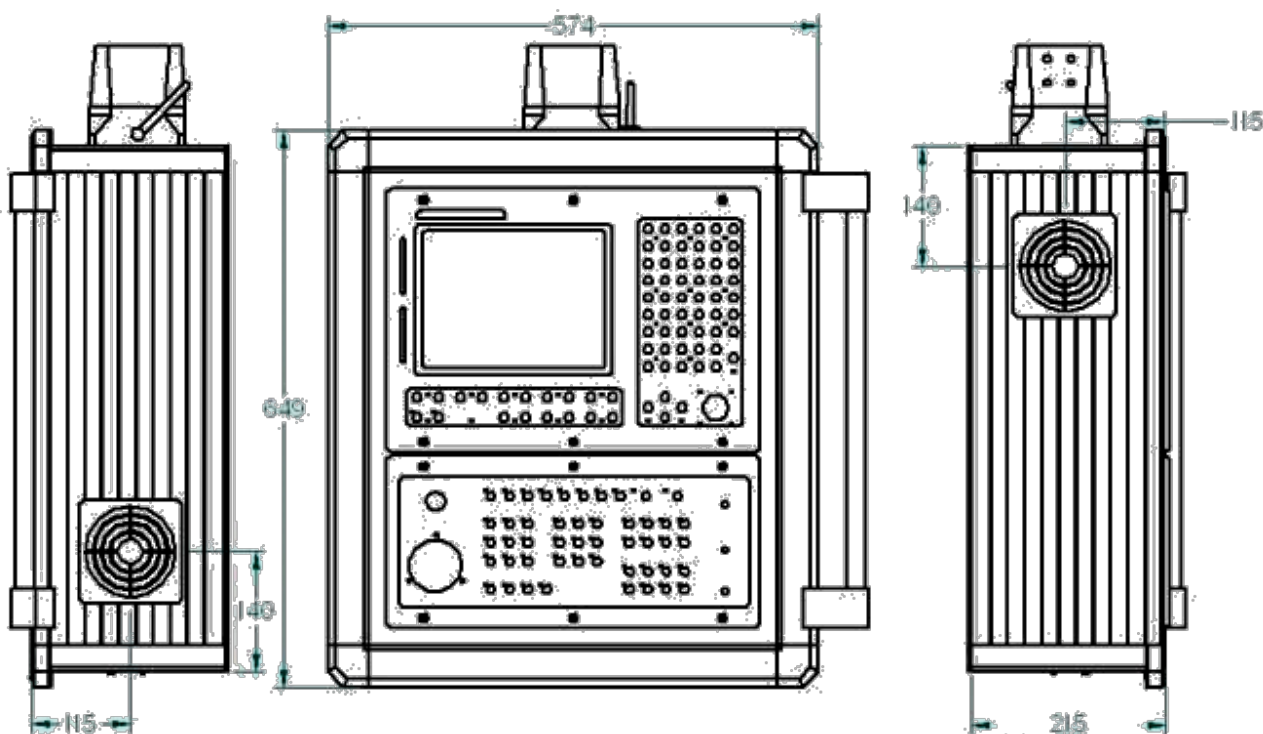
Габаритные размеры кожуха для УЧПУ NC-110.
